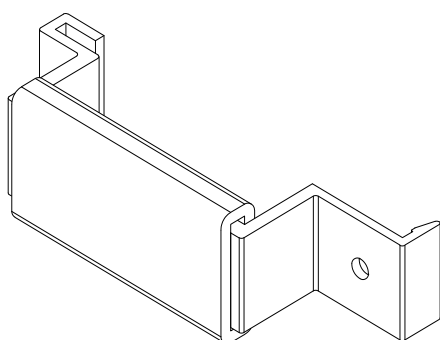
Pieza de cuelgue STB-T-CH-PRO (ref. 05.19.088)
